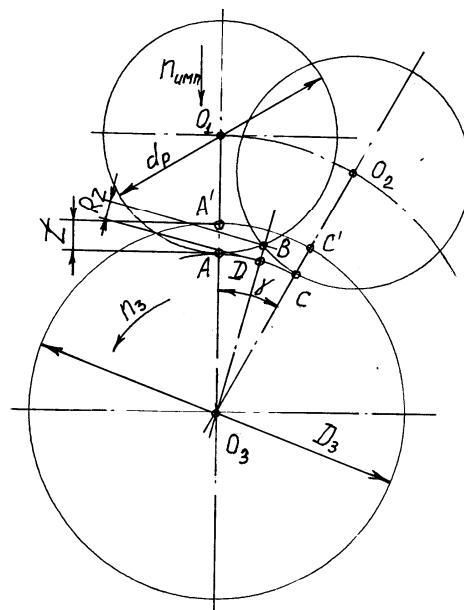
Схема статико-импульсного накатывания резьбы охватывающим инструментом с роликами для расчета шероховатости поверхности Rz :
